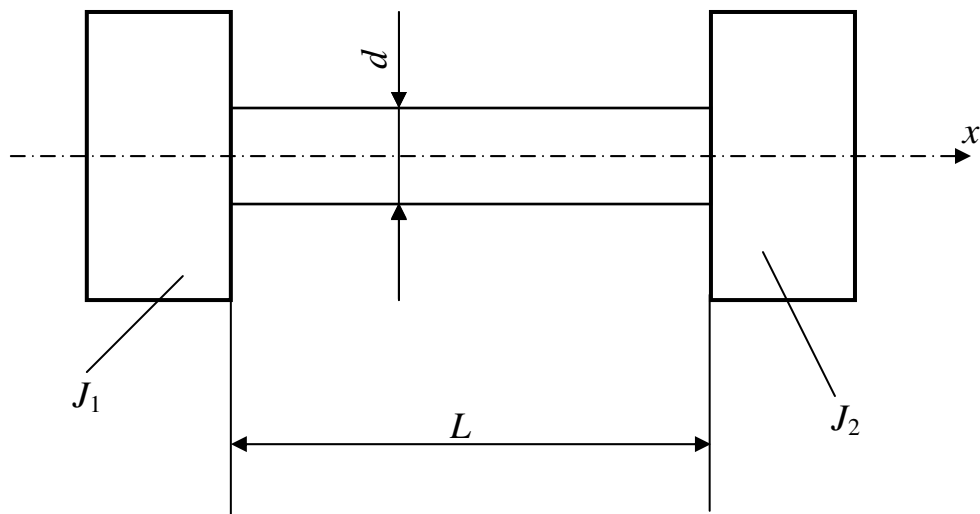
Розрахункова схема вала з двома дисками
